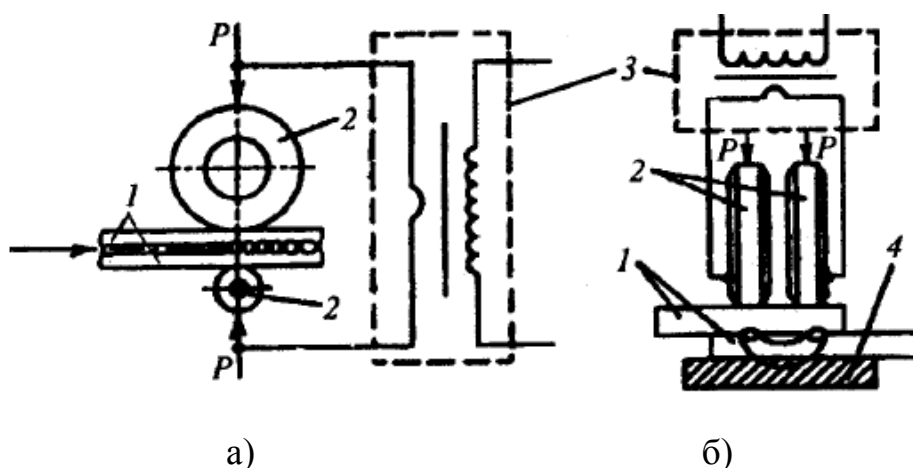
Схема шовной двусторонней (а) и односторонней (б) сварки:
